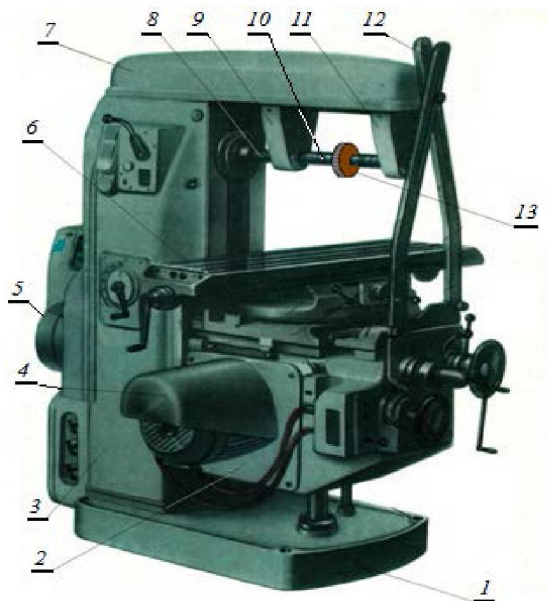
Общий вид универсального консольно-фрезерного станка модели 6Н81
